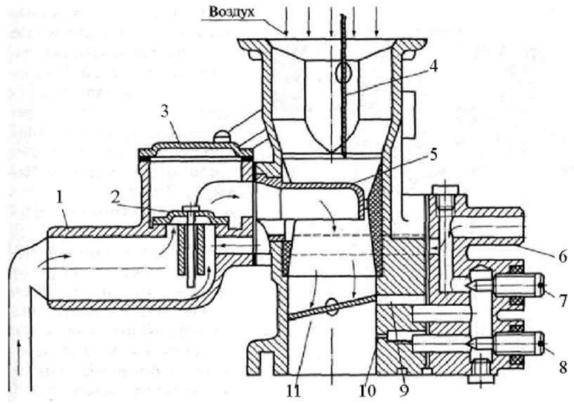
Смеситель СГ-250: 1 и 6 - патрубки подвода газа; 2 - обратный клапан; 3 — крышка; 4 - воздушная заслонка; 5 - газонаполнительное устройство; 7 - регулировочный винт переходных режимов; 8 - регулировочный винт системы холостого хода; 9 — каналхолостого хода; 10 - канал переходного режима; 11 - дроссельная заслонка.
